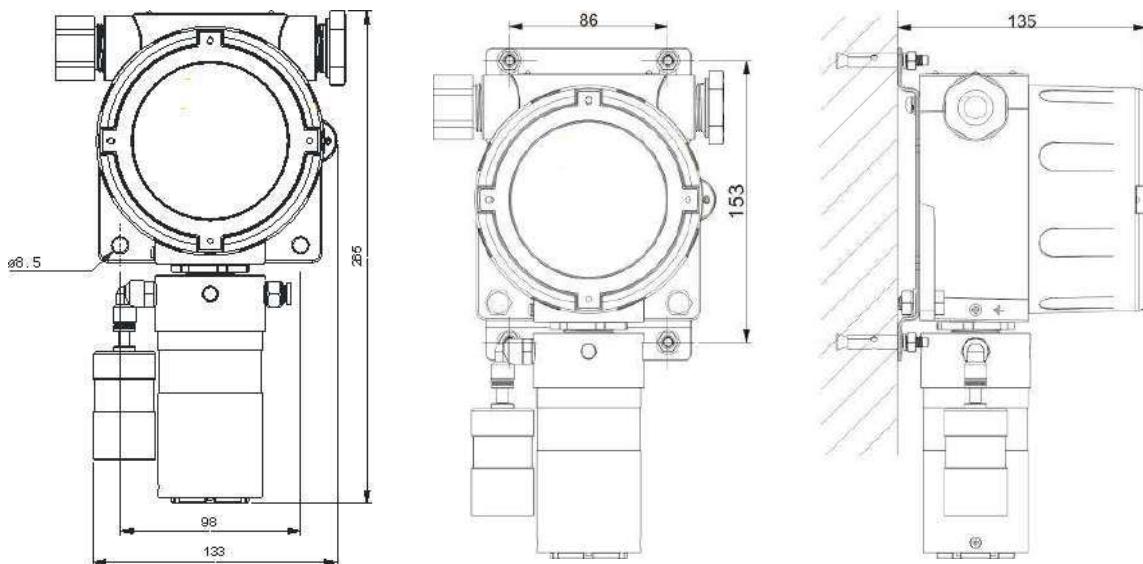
Габаритные и установочные размеры газоанализатора ЭССА-М-ИП, Ф-ИВНО
